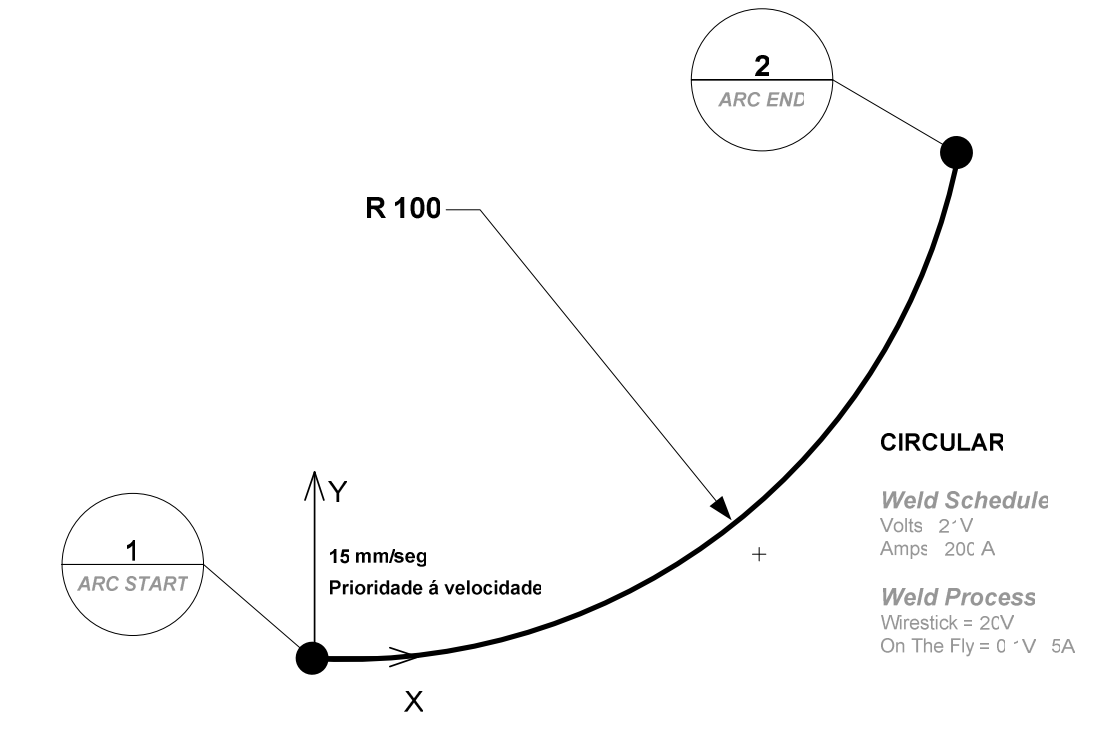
| Exercício 3 – Cordão de soldadura circular sobre um arco
